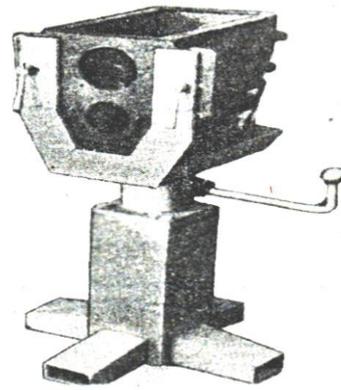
Стенд модели ОР- 12450 -01 для разборки и сборки коробок переменных передач
